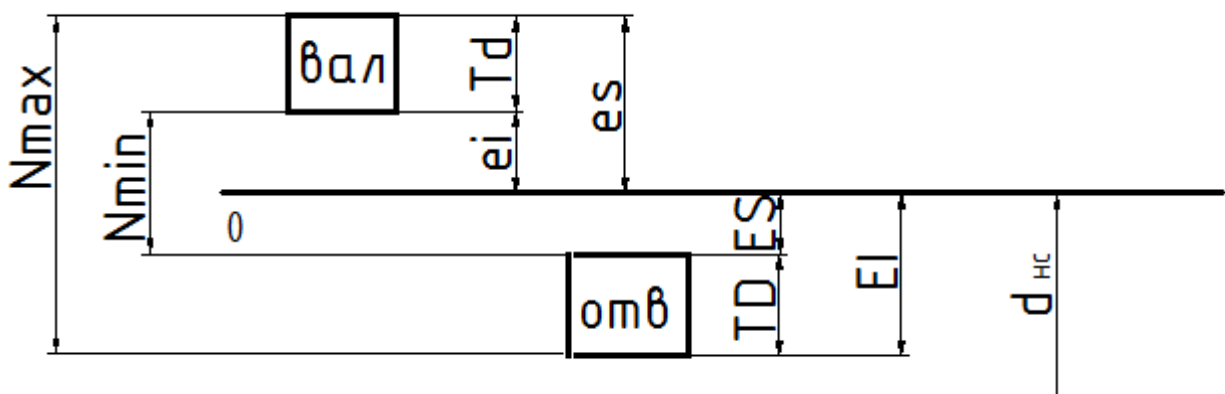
Расположение полей допусков отверстия и вала для посадки с натягом.
